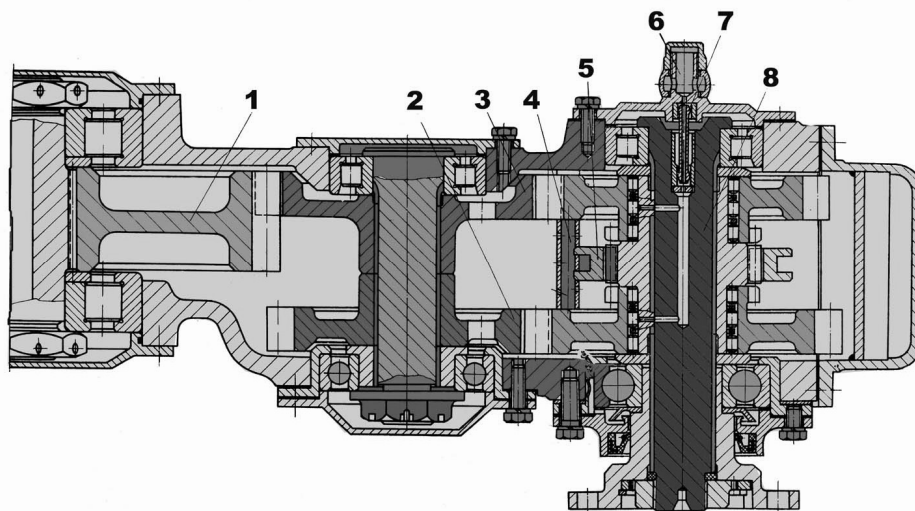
Редуктор привода вентилятора: 1 – шестерня входного редуктора; 2 и 3 – цилиндрические шестерни редуктора; 4 – разбрызгиватель; 5 – передняя муфта; 6 – трубопровод смазки; 7 – верхняя втулка; 8 – вал
